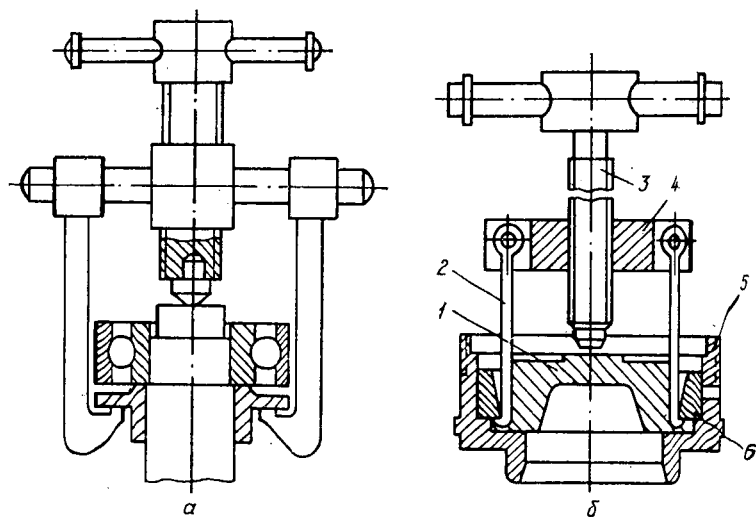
Винтовые съемники для выпрессовки подшипников:
